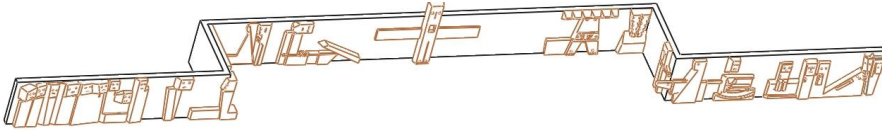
Ansicht der CAD-Baugruppe des kompletten Reliefs
